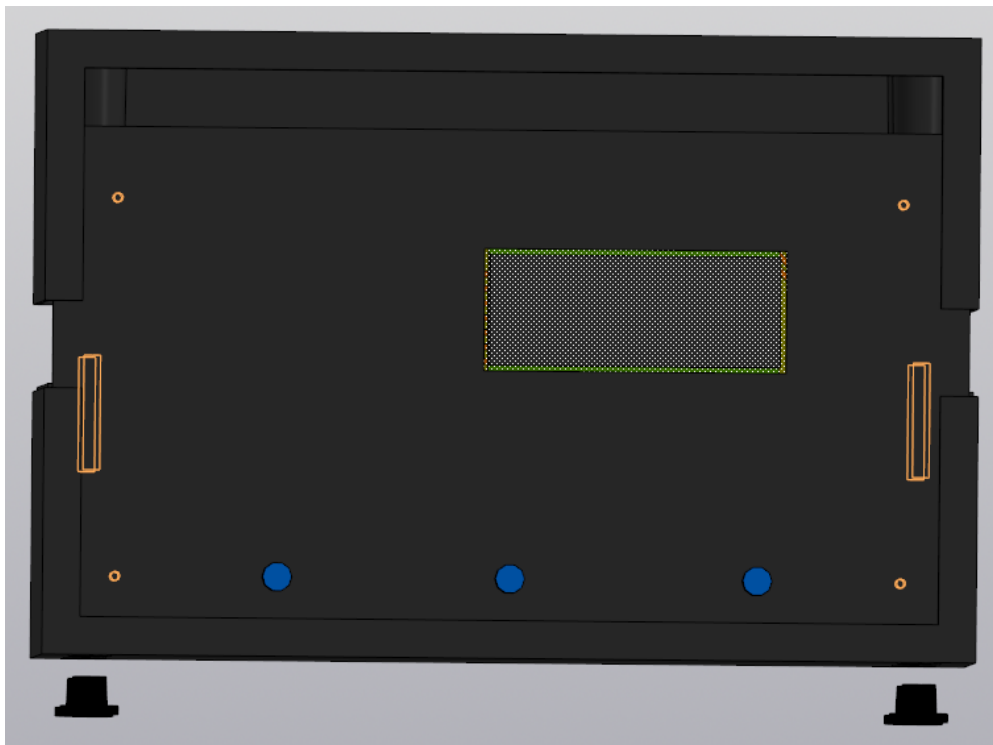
3D модель пристрою, загальний вигляд
